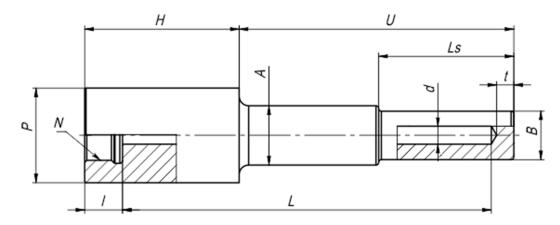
Гильза под приварку через адаптер (Socket Weld), цельноточёная, ступенчатая, под подвижный штуцер.
